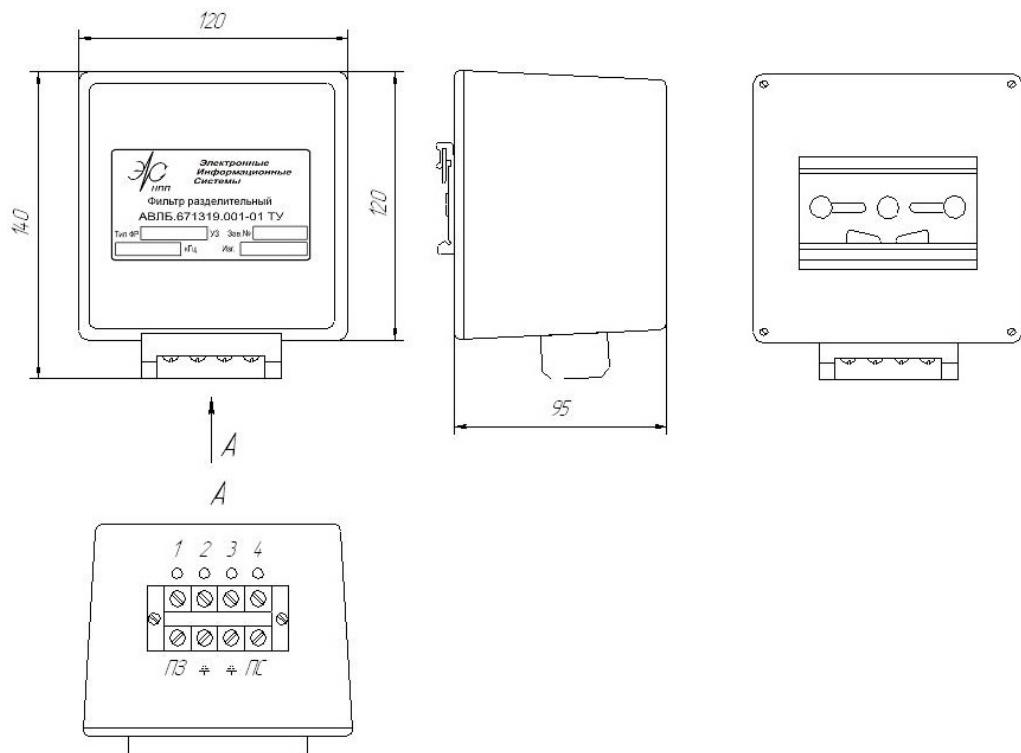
Габаритно-присоединительный чертеж фильтра присоединения ФП.
